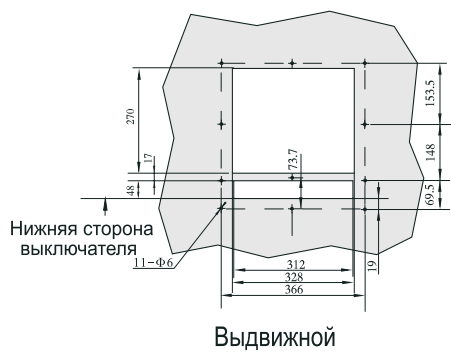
Габаритные размеры рамки обрамления выреза в двери для выключателей типоразмера F
